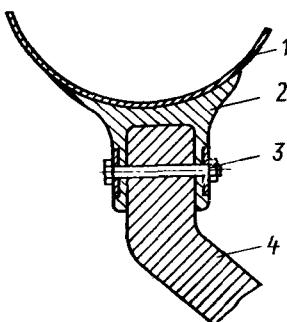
Крепление жесткого днища к надувному борту с помощью болтовых соединений
